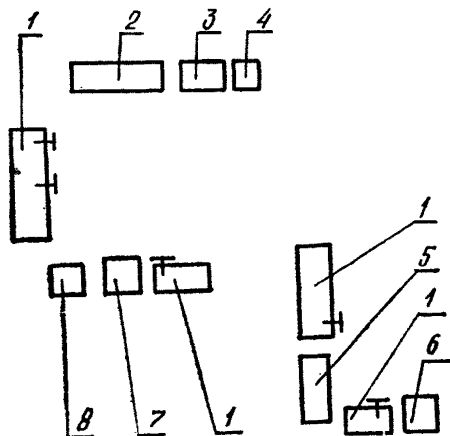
Типовая схема планировки рабочего места разборки и сборки узлов двигателя
